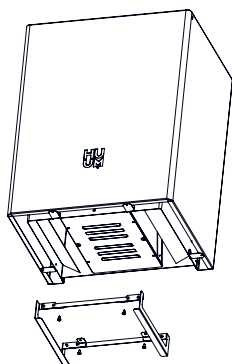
Installation des Wärmeleitblechs bei HUUM CORE Wall und CORE Wall Mini.
